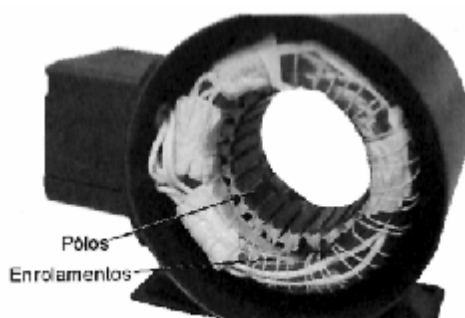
Aspecto do estator de um motor industrial de CC sem escovas.
